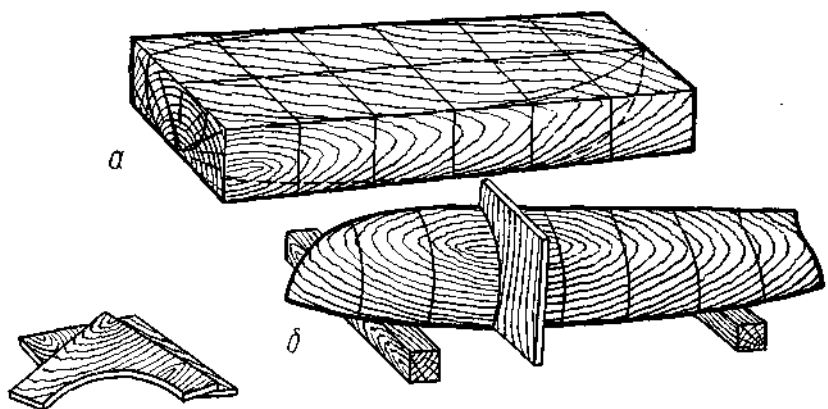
Разметка бруска дерева (а) и обработка корпуса по шаблонам шпангоутов (б)
